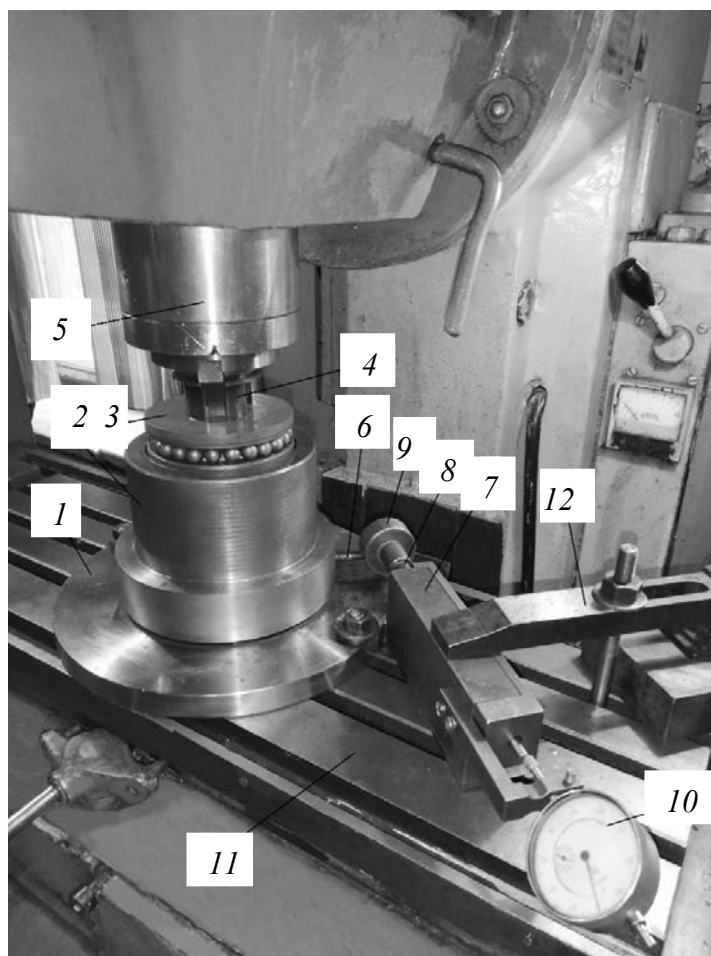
Устройство для определения момента, создаваемого деформирующими шарами комбинированного инструмента при СМДН: 1 – основание; 2 – ферромагнитный цилиндр; 3 – инструмент; 4 – оправка; 5 – шпиндель; 6 – планка; 7 – корпус динамометра; 8 – плунжер; 9 – сферическая опора; 10 – индикатор; 11 – стол станка; 12 – элементы крепления корпуса динамометра
